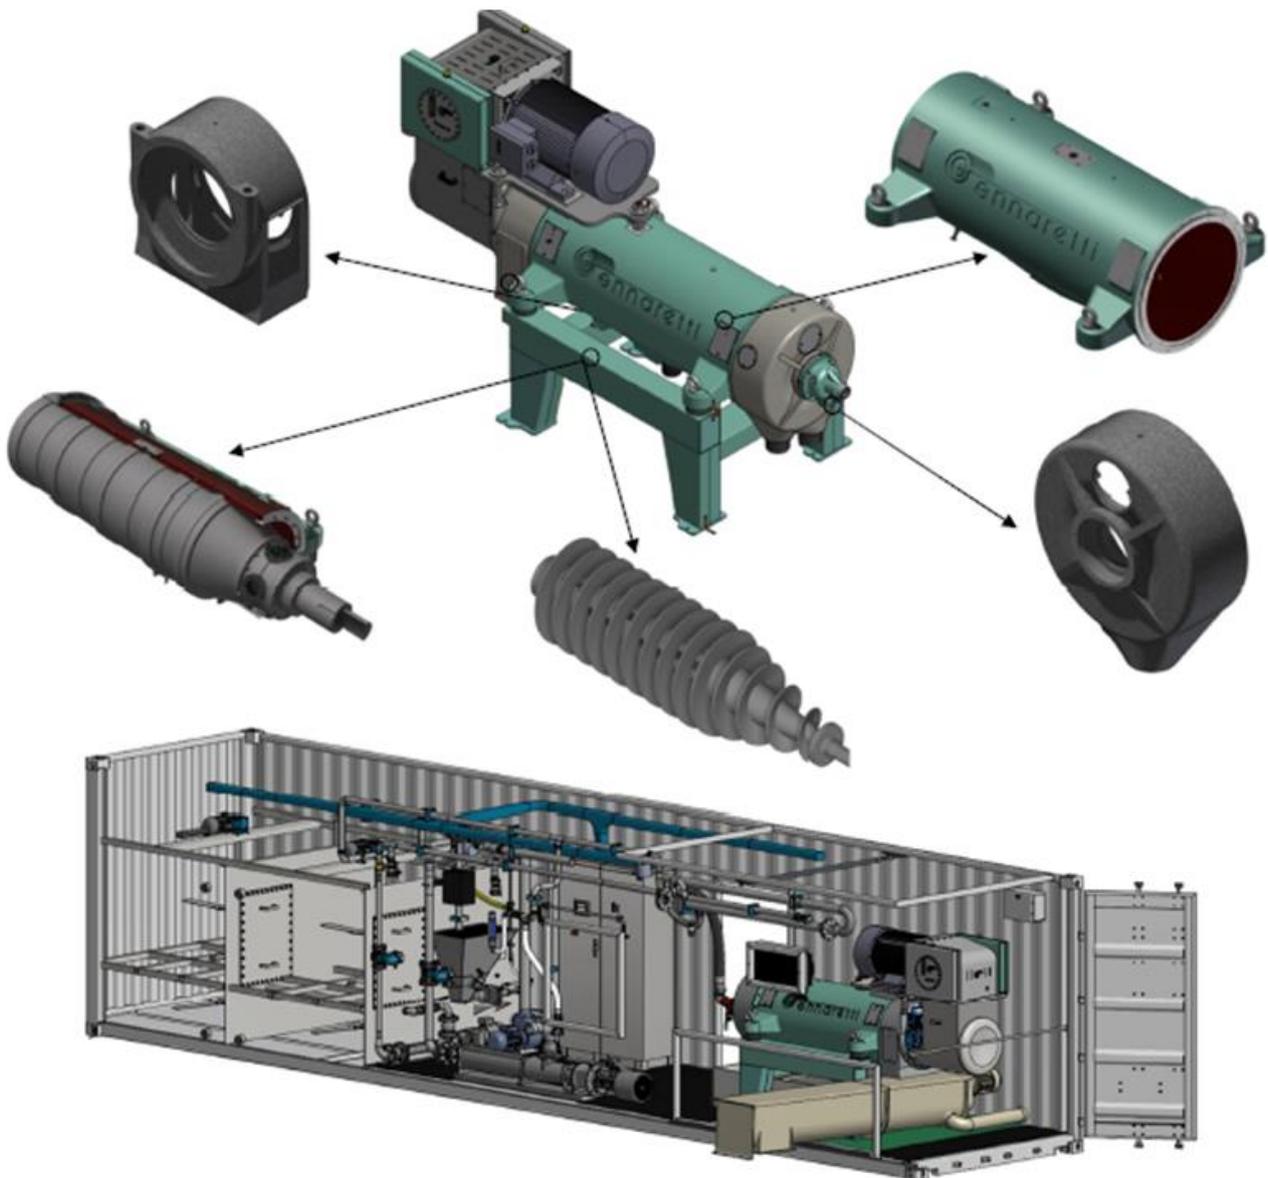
schema strutturale della centrifuga e dell'impianto di ispessimento.
